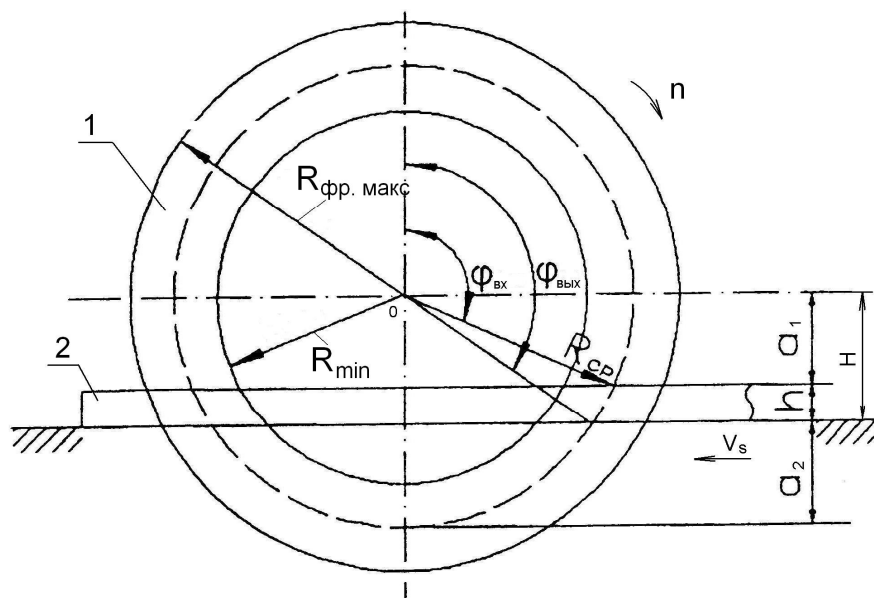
Схема фрезерования: 1 – фреза, 2 – заготовка
